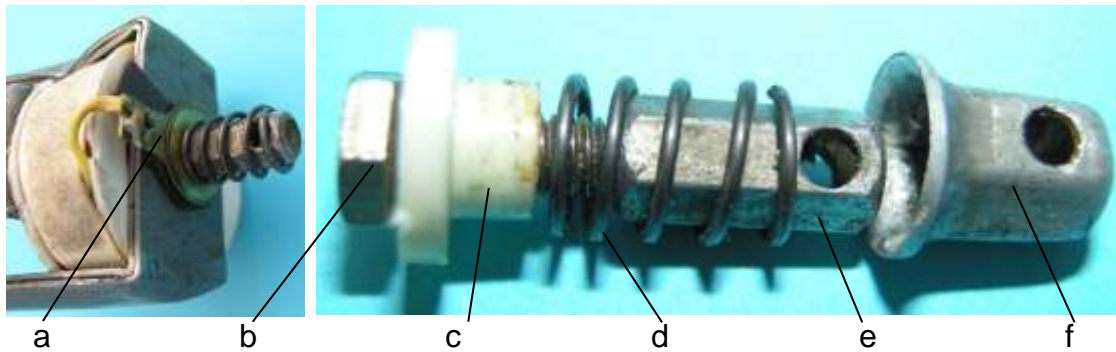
Kontaktsystem: a) Spulenanschluss, b) Kontaktbolzen, c) Isolierung zum Ankerblechpaket, d) Schraubenfeder zur Herstellung des Drahtkontakts, e) Kontaktelement mit Innengewinde und Durchgangsbohrung für den Drahtanschluss, f) Kontaktkappe mit Bohrung
